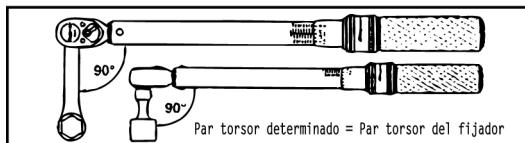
utilización de extensiones oscilantes y accesorios universales con las llaves dinamométricas.
